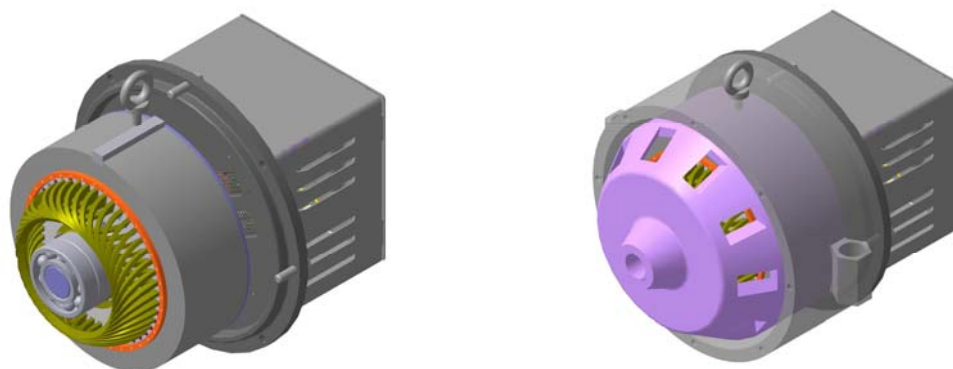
Взаимное расположение ротора и статора в двигателе.
